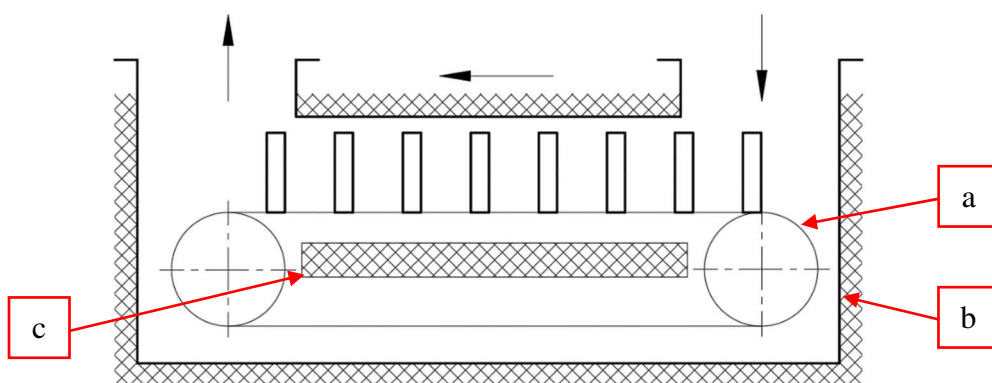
Přípravek pro testování metody ohřevu a chlazení
